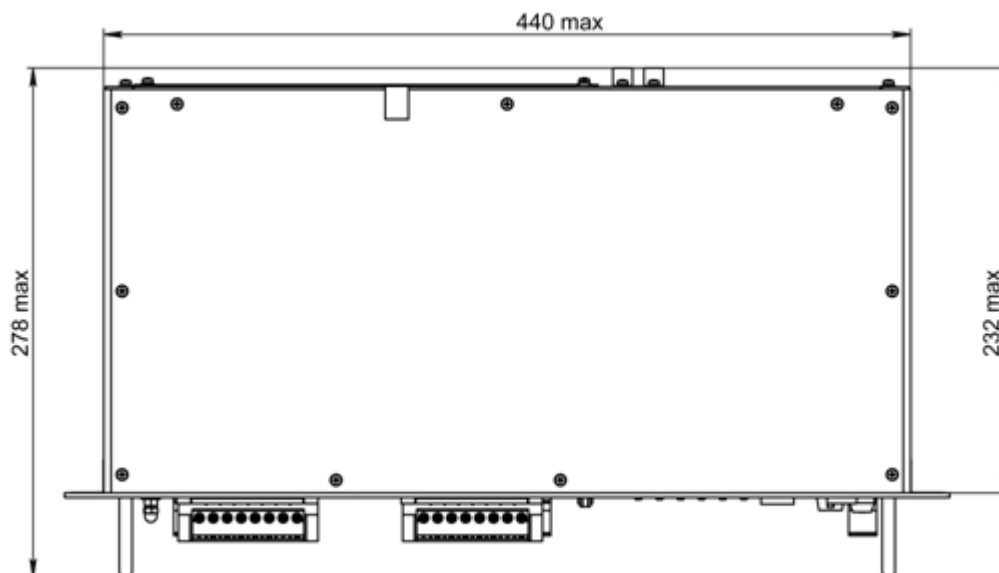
Габаритные размеры регистратора вид сверху
